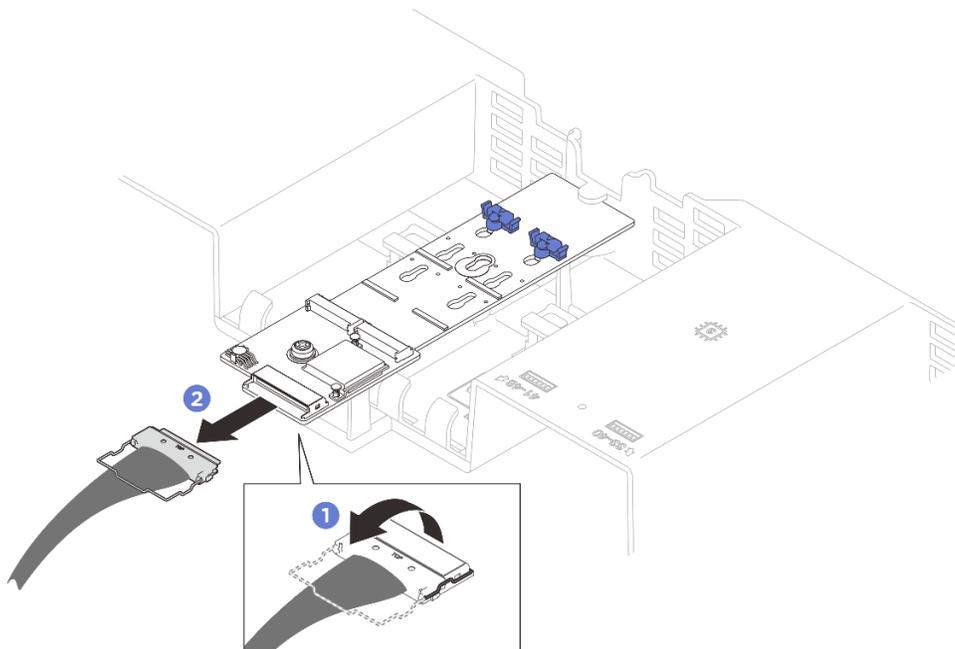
Desconexión de los cables del adaptador de arranque M.2
